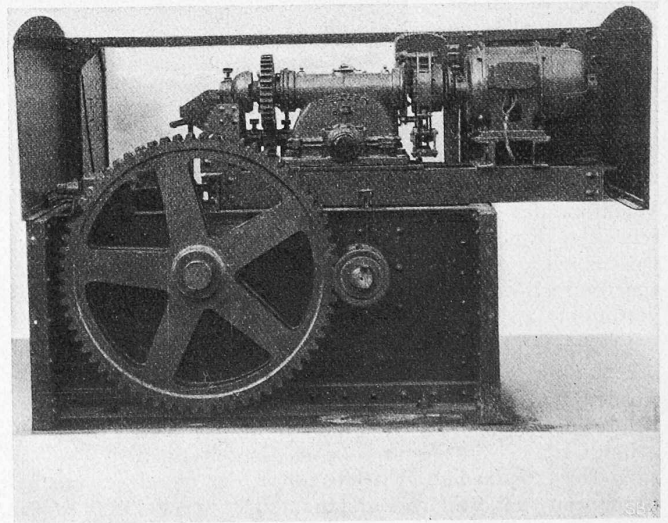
Windwerk einer Spülschütze (Gehäuse geöffnet).
